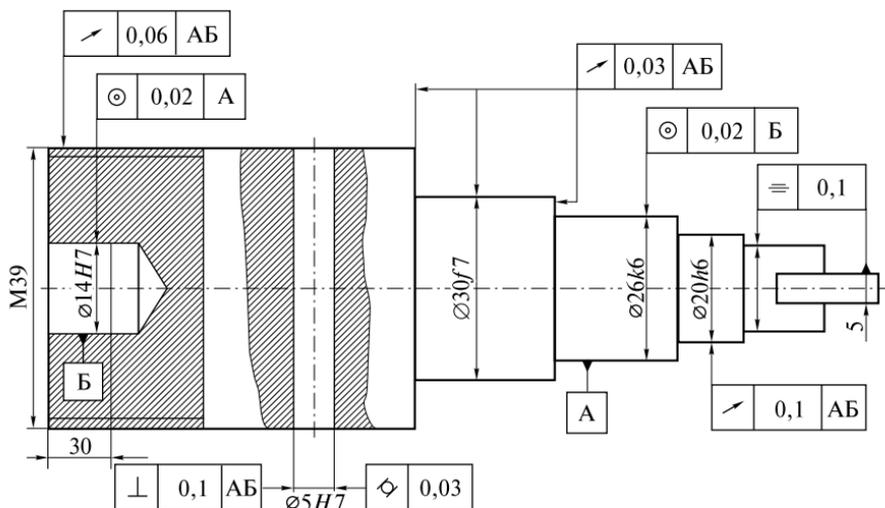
Допуски формы и расположения поверхностей на детали типа «вал»
